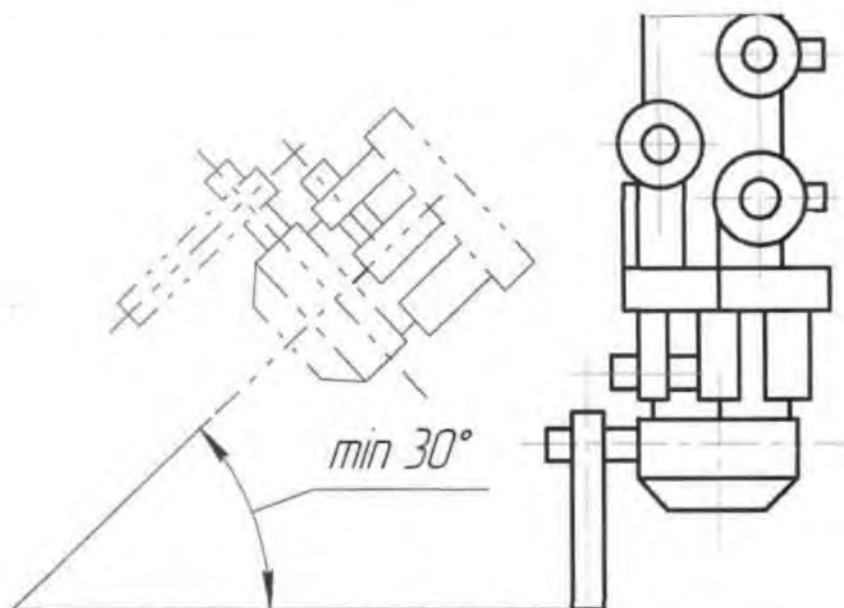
Наклон мундштука сварочной головки
